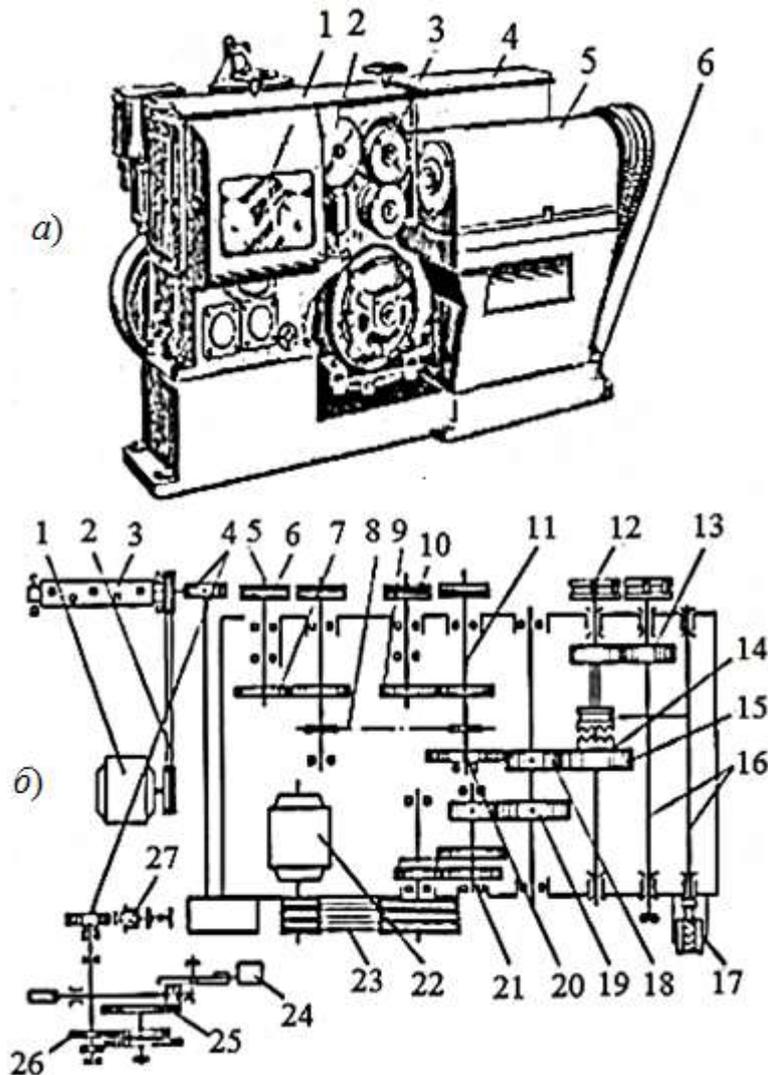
Станок для одновременной правки и резки арматурной стали с непрерывной подачей: *а* – общий вид; *б* – кинематическая схема.
